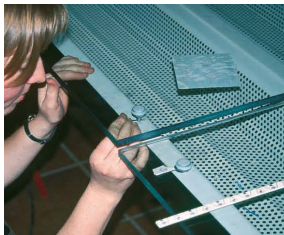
a, b,c,d) Detalji kod staklenih konstrukcija (N, Rob,st.80; S.Behling,st. 85; J.Wurm, st.173; N, Rob,st.33)
